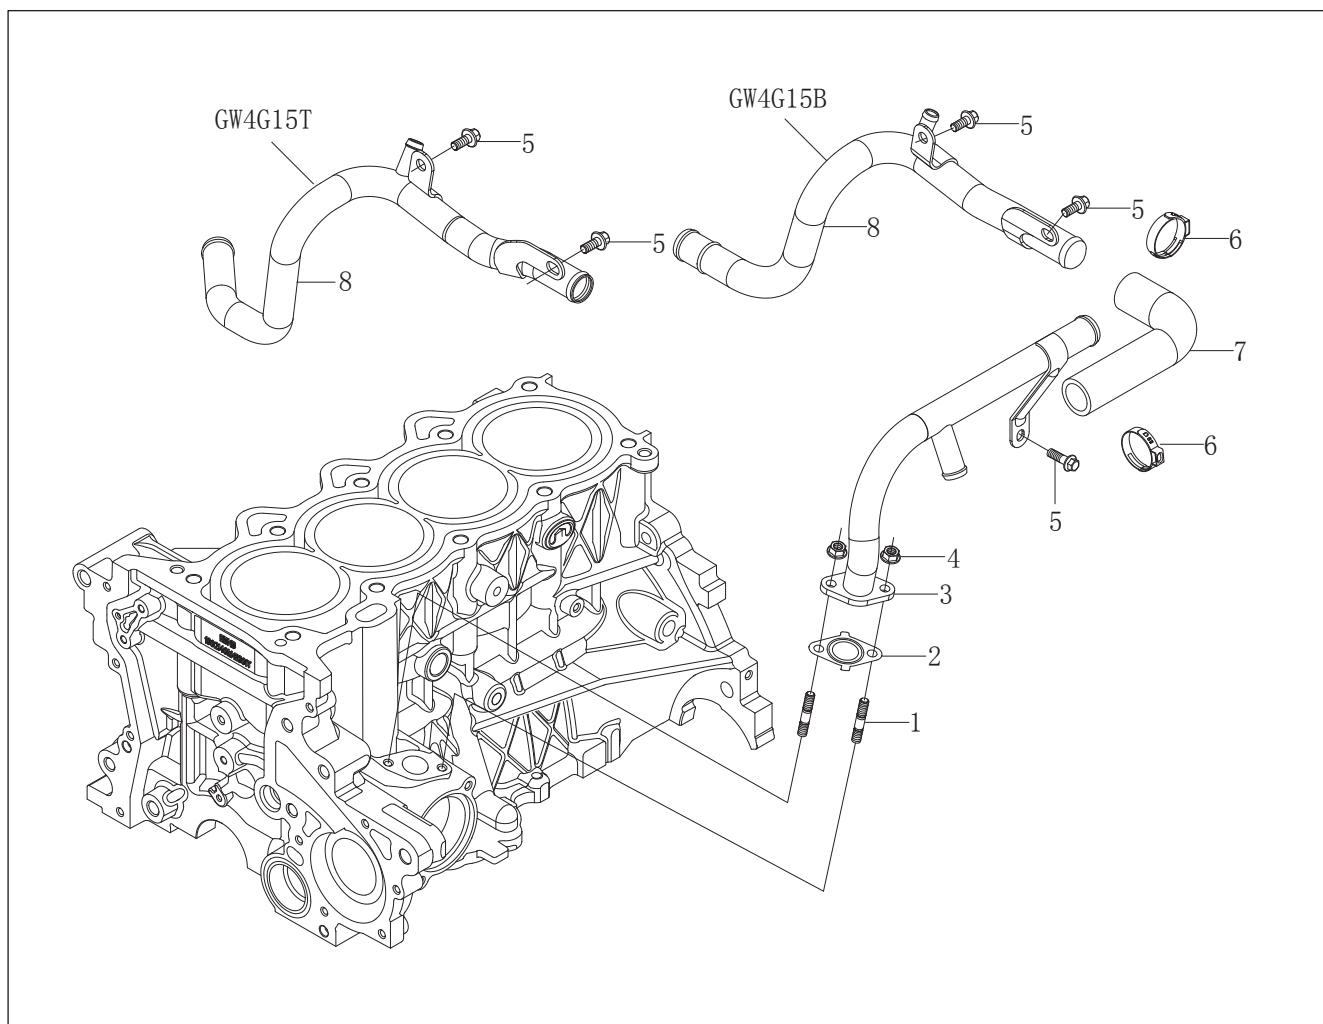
Сборочная схема деталей отводящей трубы нагретой ОЖ
